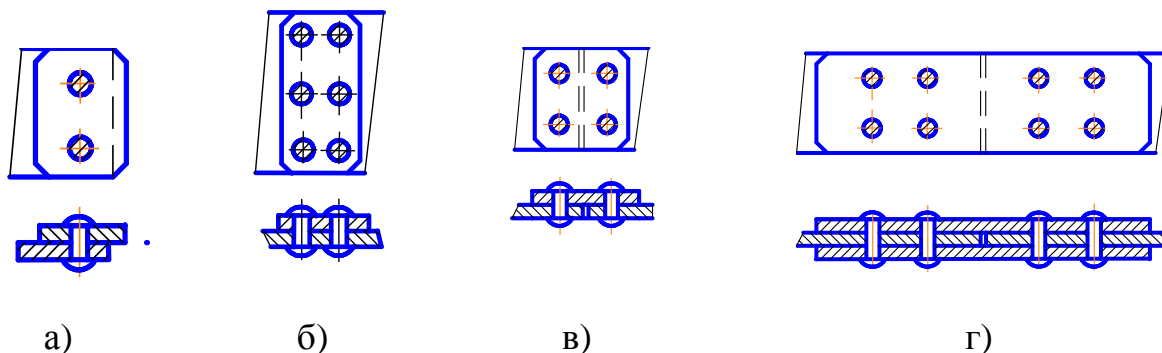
Конструкции заклепочных швов: а) - однорядный заклепочный шов внахлестку; б) - двухрядный заклепочный шов; в) - соединение двух листов встык с одной накладкой; г) - соединение с двумя накладками.
